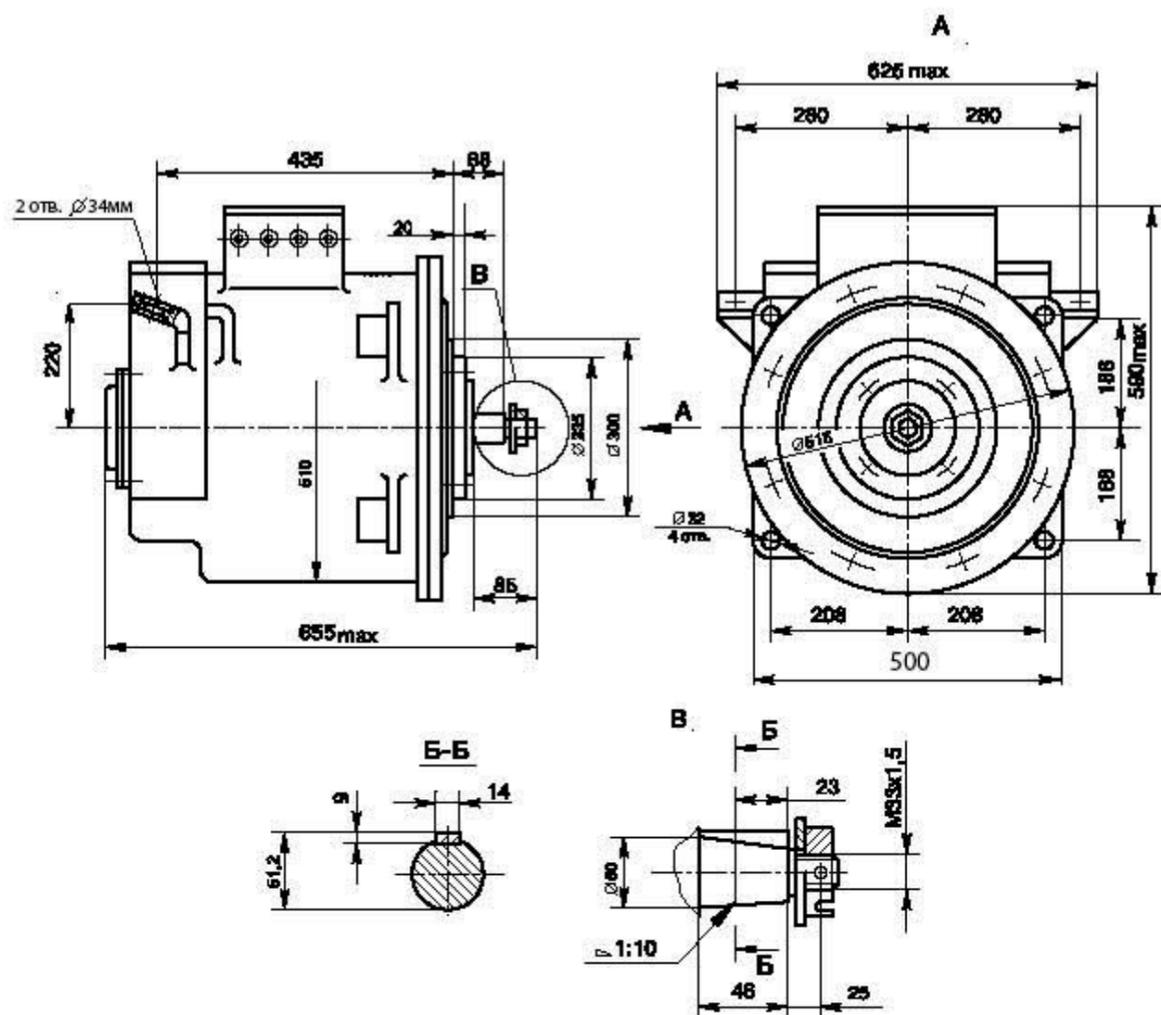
Габаритные и установочные размеры электродвигателя ДРТ-33
